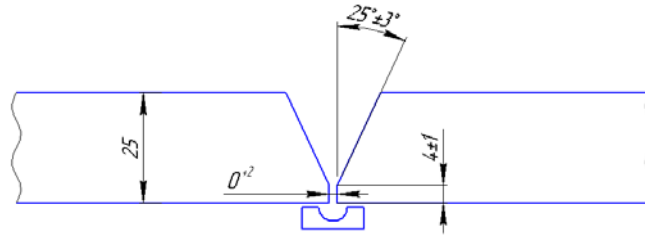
Схема сборки стыка полок под сварку
